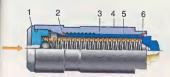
Гидронатяжитель: 1 – клапан; 2 – запорное кольцо; 3 - плунжер; 4 - корпус; 5 - пружина; 6 - стопорное кольцо.
